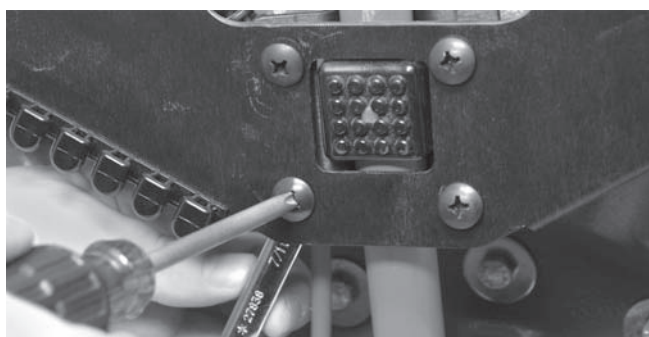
Podłączenie przewodu systemowego przed montażem
